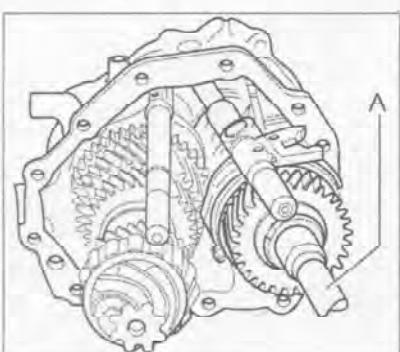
Извлеките из корпуса подшипников первичный вал (А) со штоком и вилкой включения 3-й/4-й передач.
